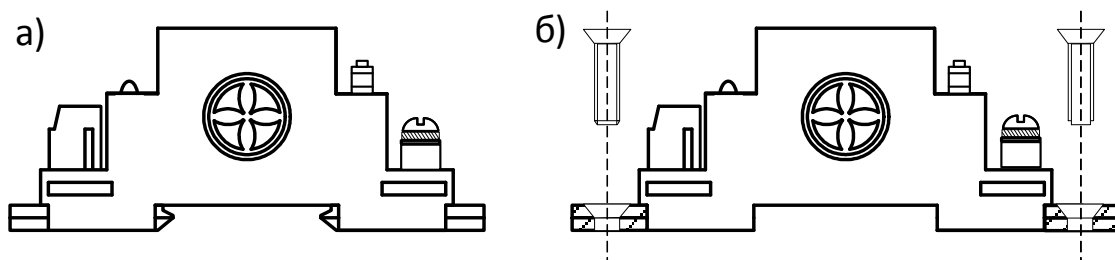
Способы крепления устройств Commeng Compact OVP (а-на рейку DIN, б-к поверхности).
